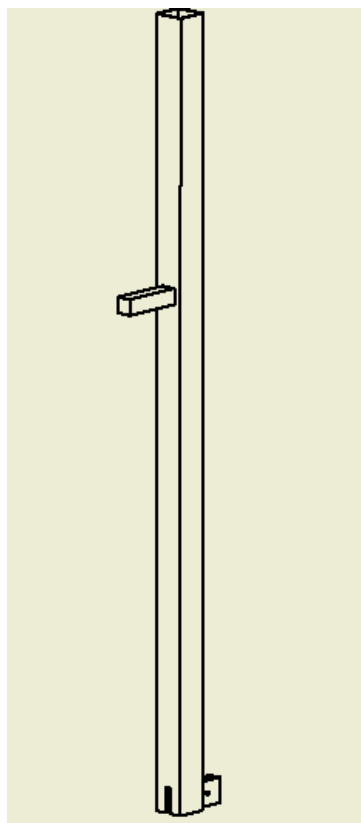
Эскиз рамы ленточной пилы с указанными местами разборки конструкции
